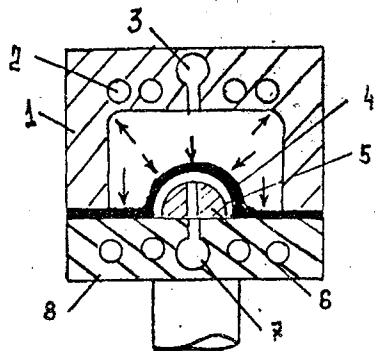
Формование под давлением в прессе: 1 — верхняя плита прессы; 2 — нагреватели; 3 — коллектор для подачи сжатого газа; 4 — диафрагма; 5 — заготовка; 6 — форма; 7 — коллектор для соединения с атмосферой или вакуумом; 8 — нижняя плита прессы
